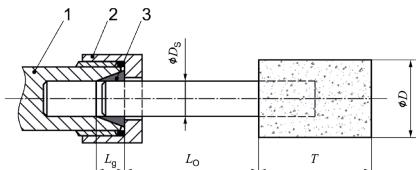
Lunghezza di bloccaggio del mandrino di serraggio e della pinza portautensili
